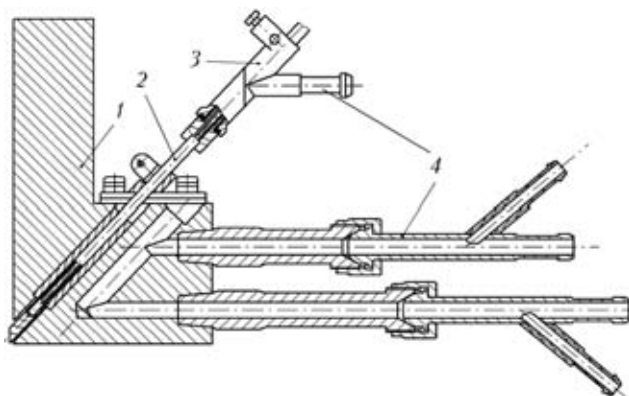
Схема передней накладки с датчиком оплавления кромок: 1 — формирующая накладка; 2 — щуп; 3 — корпус щупа; 4 — система охлаждения
